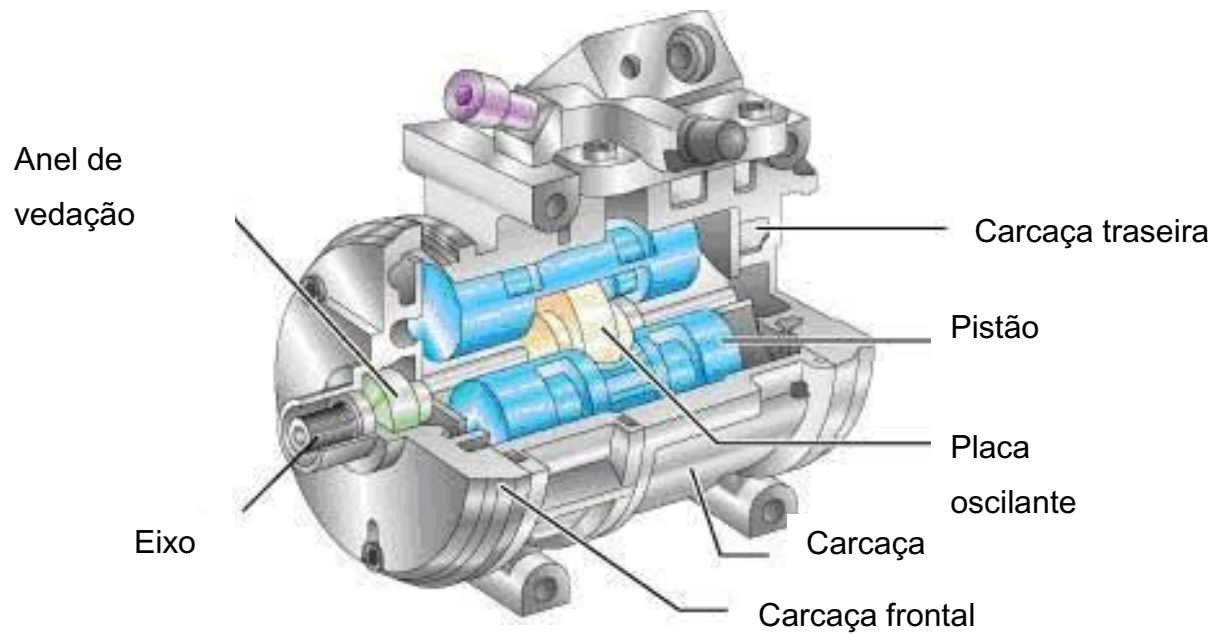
Desenho de compressor fixo tipo placa oscilante. Fonte: Air International Catalogue
